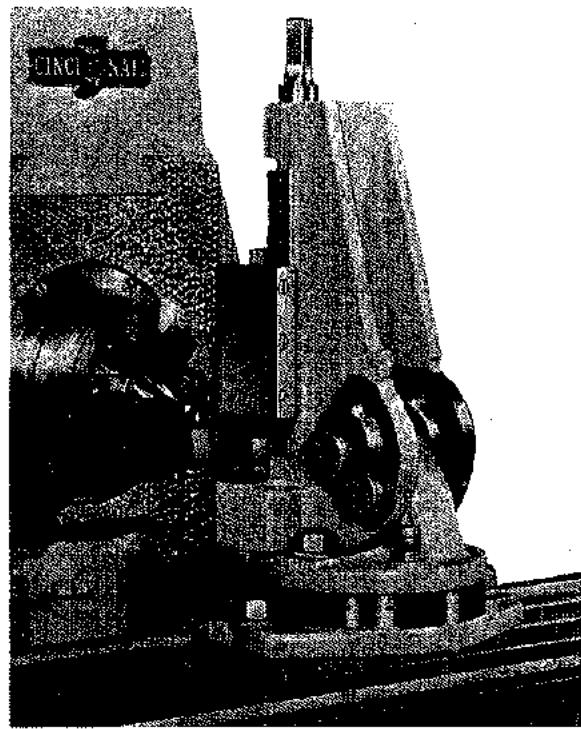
Tornillo de mordazas universal (Cincinnati Milling Machine Co.)
